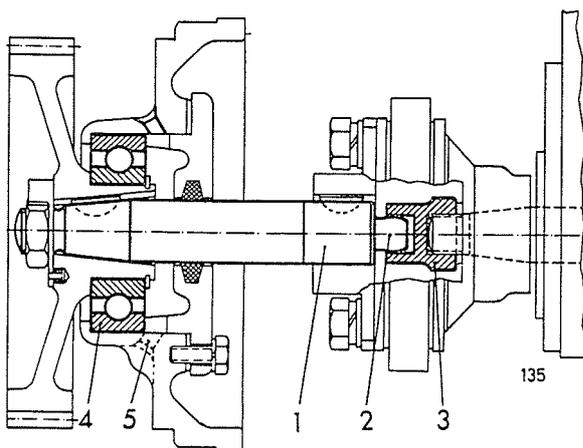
Einspritzpumpenantrieb F/A 4-6L 514
